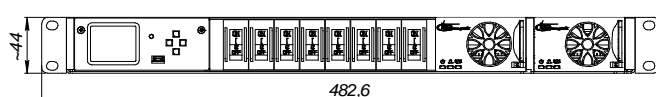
Габаритный чертеж УЭПС-7К 48/74 (60/60)-22-T
